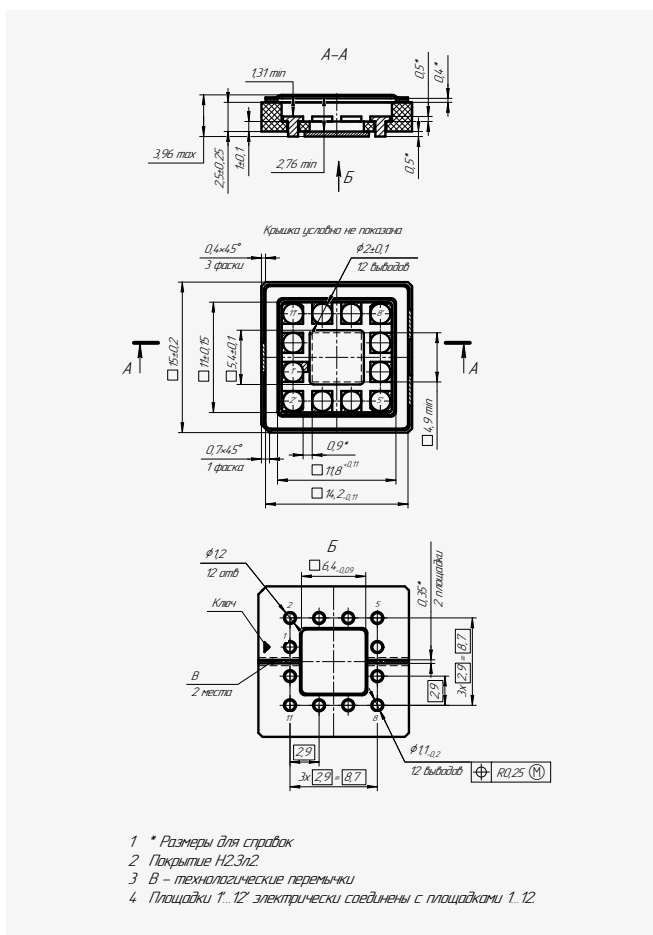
Габаритный чертёж металлокерамического корпуса КТ-119-1
